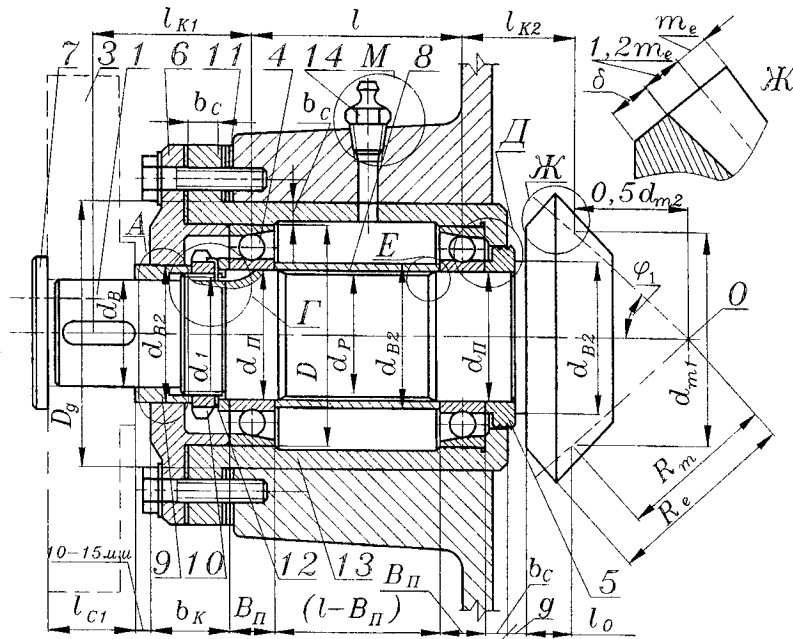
Вал-шестерня кінчної закритої зубчатої передачі (варіант опор “у розпір”)
